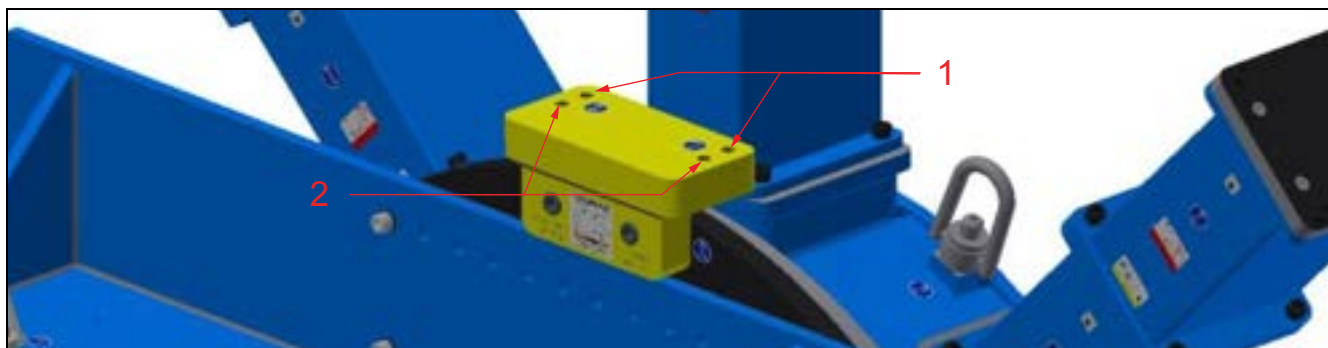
LEVAGE DE L'ENSEMBLE SUR LA MACHINE
